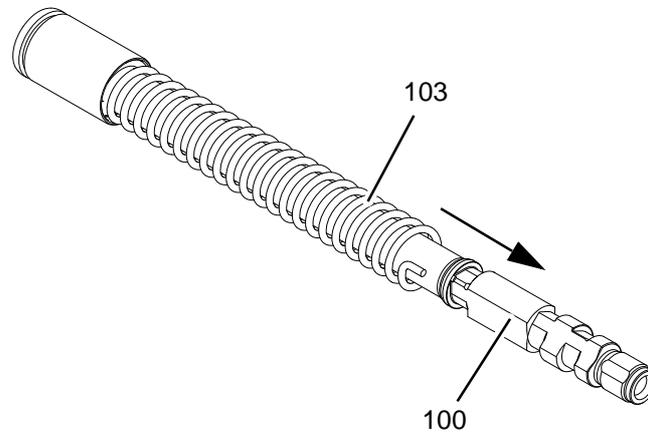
Retirer le ressort de la marche tournante du tube de guidage
